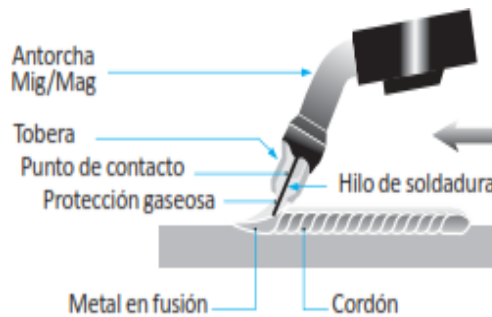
Representación esquemática del proceso de soldadura GMAW
